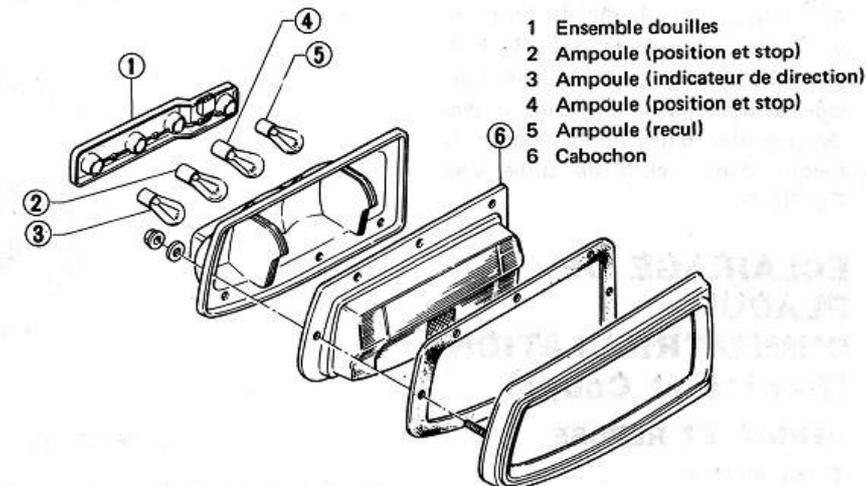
Feu arrière combiné (Berline et Coupé)
